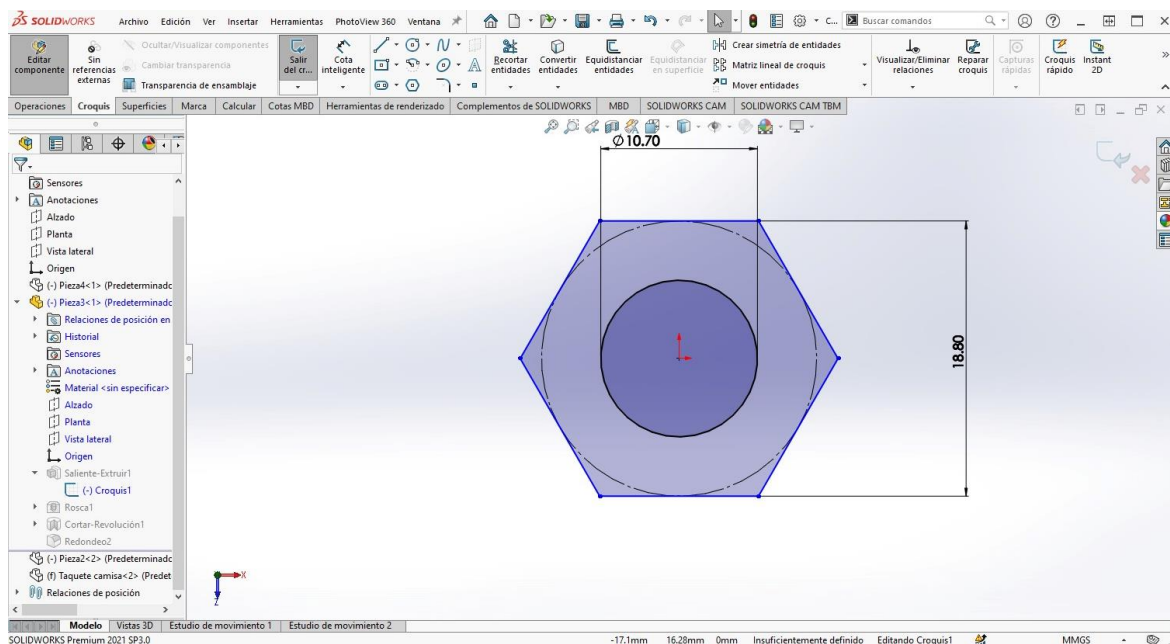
Croquis base de la tuerca hexagonal con dimensiones principales.
